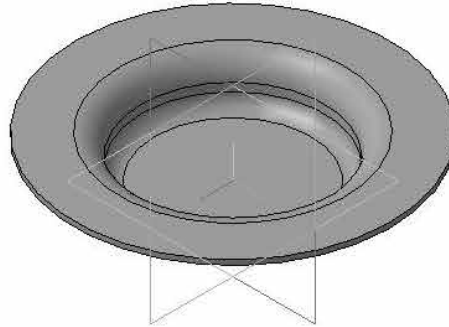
Твердотілова параметрична модель заготовки фланця
